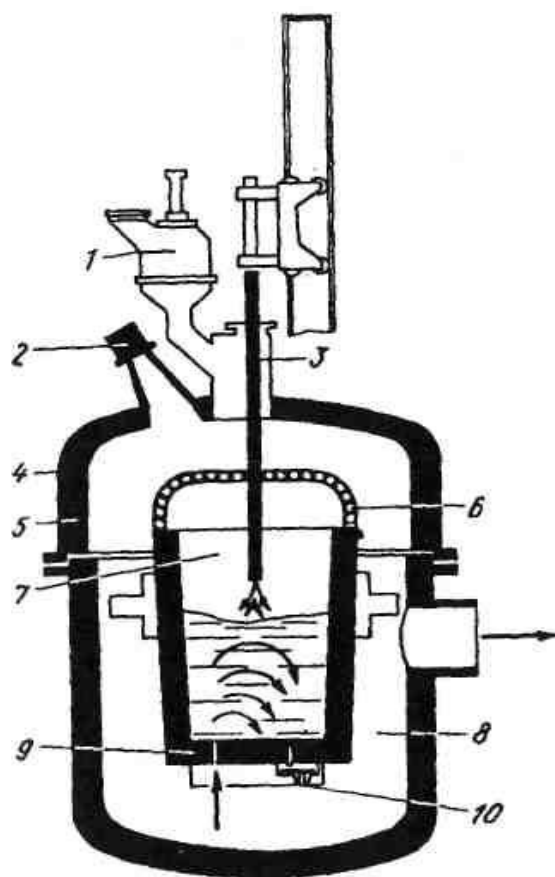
Общая схема камерного вакууматора: 1 – шлюзовое устройство; 2 – смотровое стекло с ротором; 3 – кислородная фурма; 4 – водоохлаждаемый экран; 5 – стационарный теплозащитный экран; 6 – крышка ковша; 7 – сталеразливочный ковш; 8 – вакуум-камера; 9 – пористый блок; 10 – шиберный затвор ковша
